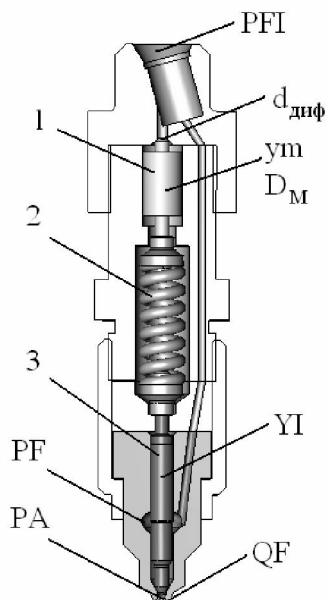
Форсунка для двухфазного впрыскивания топлива:
